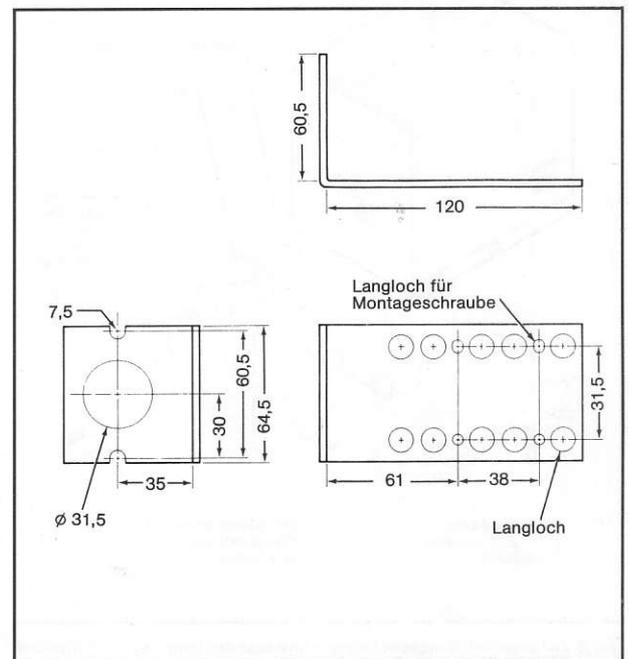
Maße der Montageplatte T. Nr. 126809 (mm)
